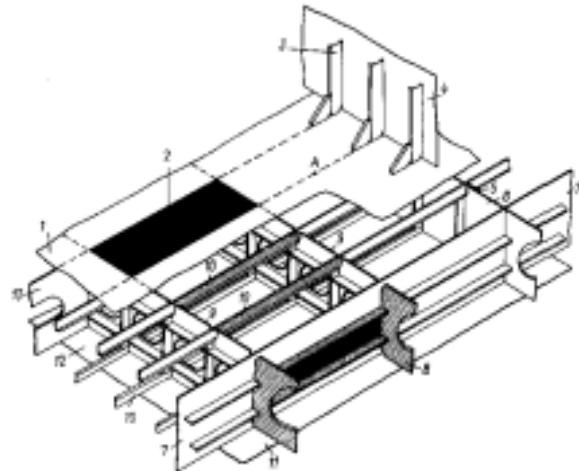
Двухъярусное перекрытие с продольным системой набора
